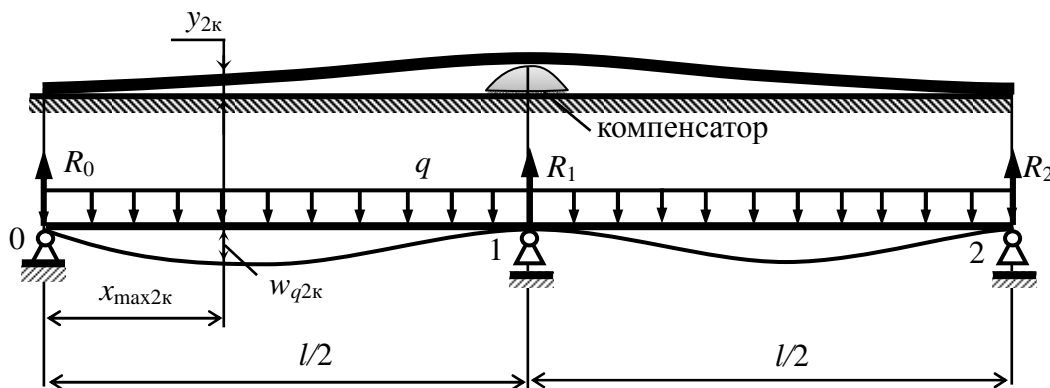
Расчётная схема заготовки при закреплении магнитным полем стола станка с одной парой компенсаторов
